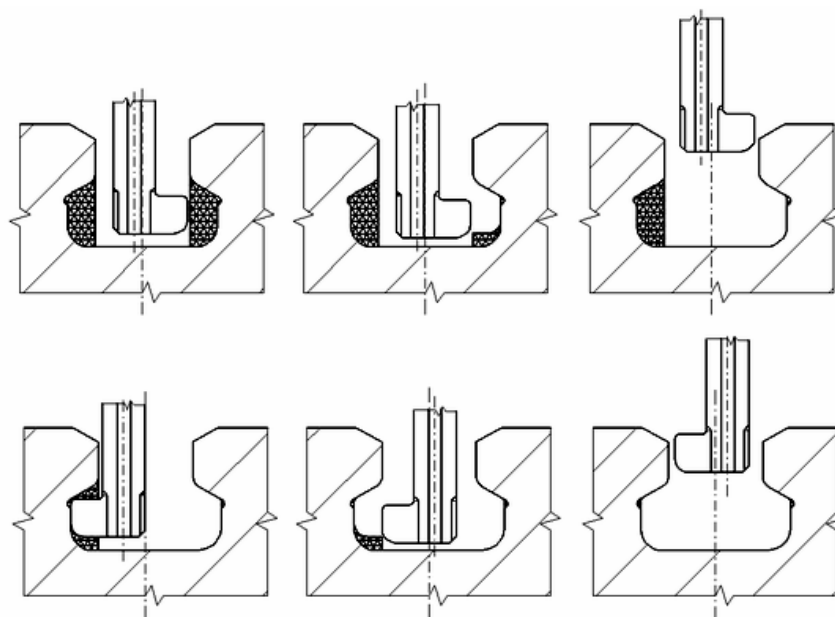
Postup při soustružení krčku a kapsy drážky
